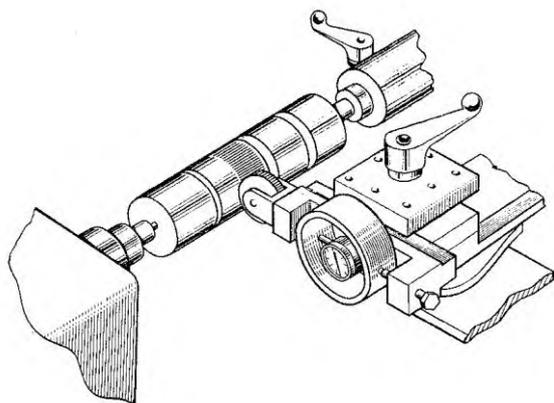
Накатка шейки вала на токарно-винторезном станке
